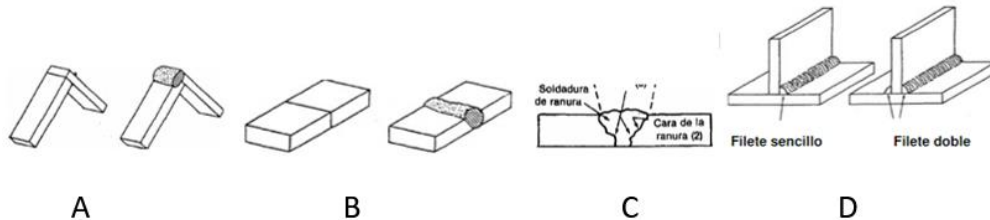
A. Unión de Esquina, B. Unión a Tope, C. Soldadura Ranura, D. Soldadura Filete. [7]
